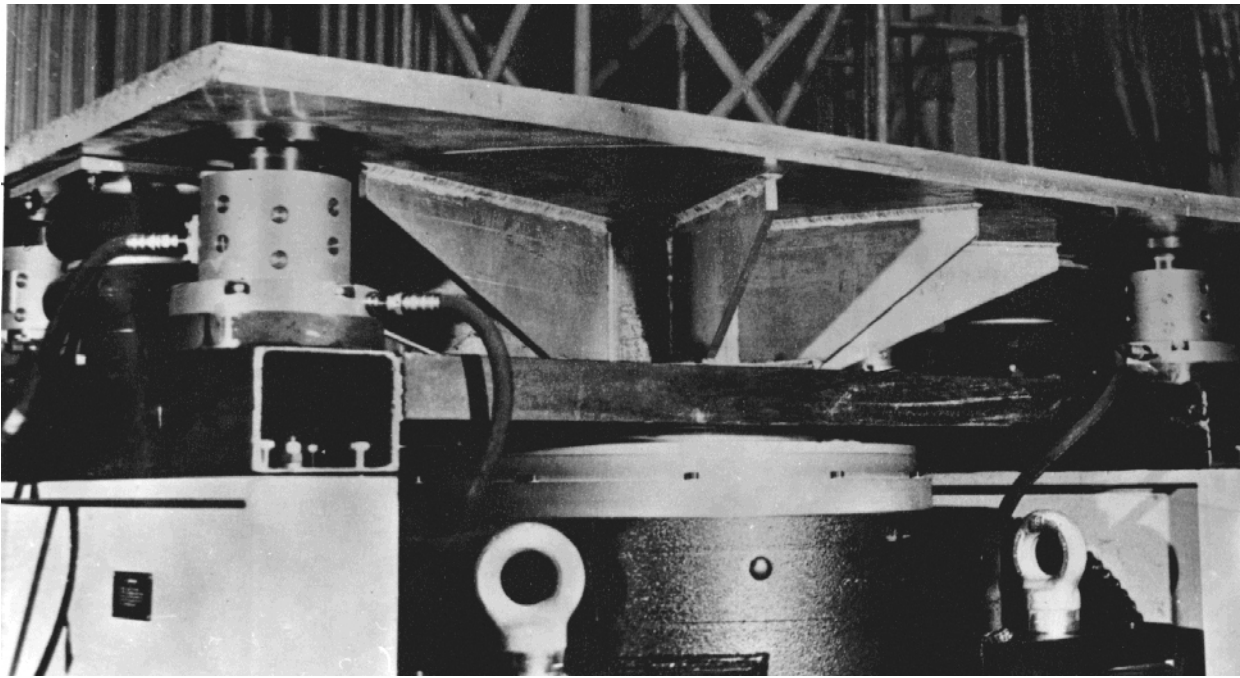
Общий вид разгрузочного устройства с ПРКО и ГСН для ЭДВУ типа V 980
